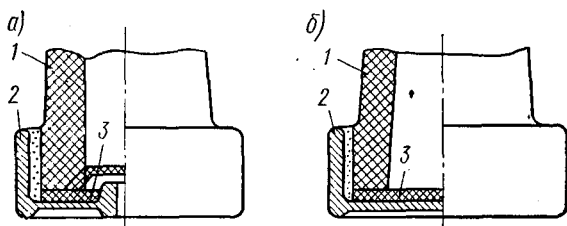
Армирование крупных фарфоровых изоляторов
